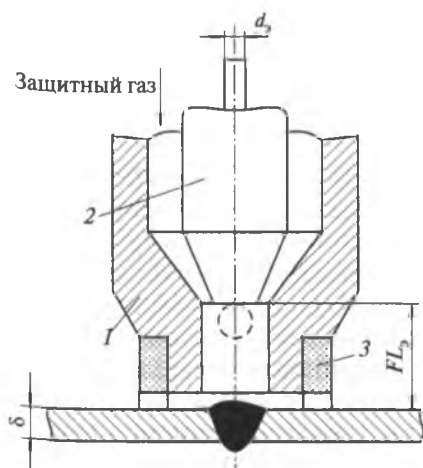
Схема процесса дуговой точечной сварки:
